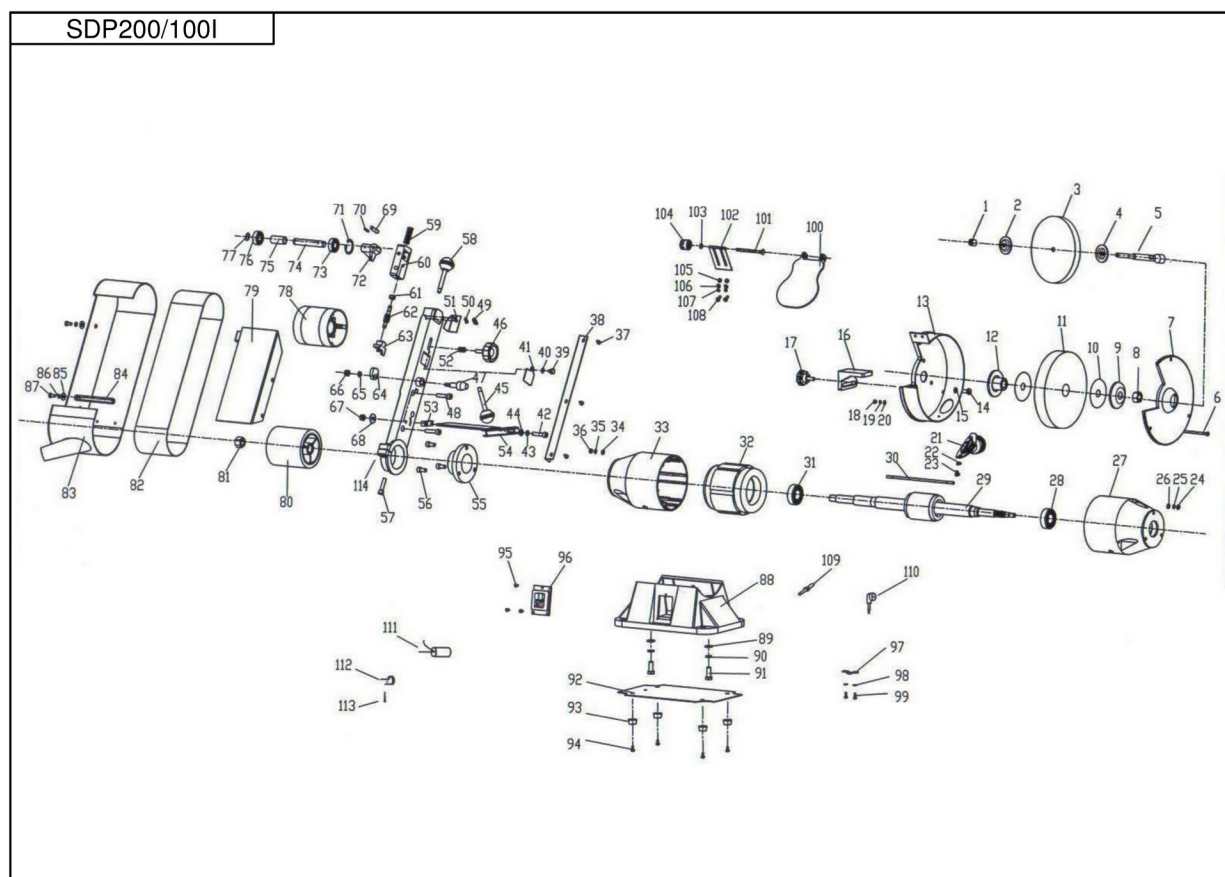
Vue éclatée de l'AY-200 IND LJ
